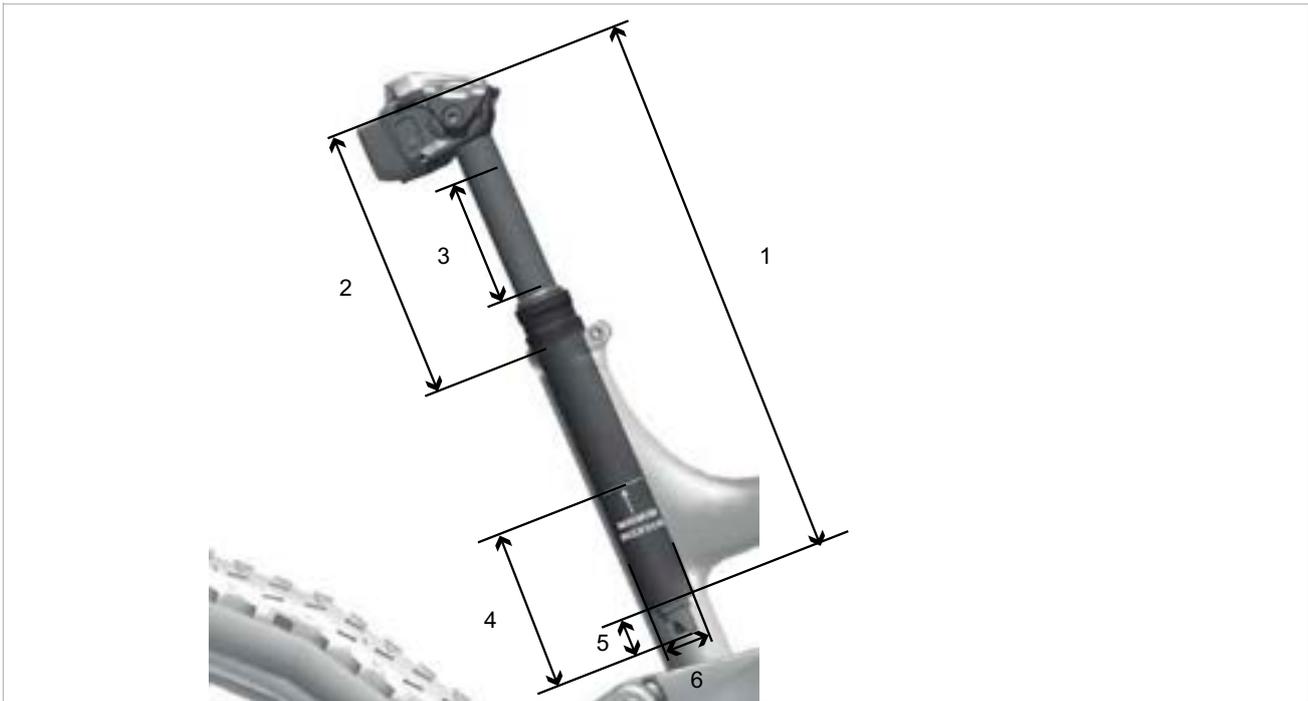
Dimensions de la tige de selle ROCKSHOX, Reverb AXS™
